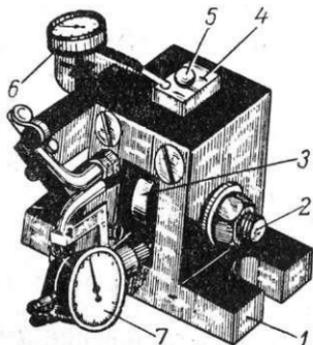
Приспособление для получения отпечатка на цилиндрической поверхности образца.
